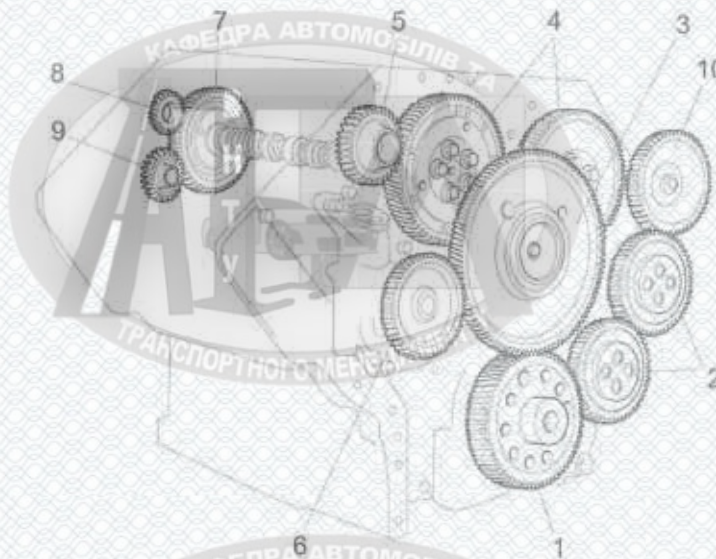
Особливості конструкції газорозподільного механізму, що використовується на V – подібних двигунах SCANIA: 1 - шестерня колінчастого валу; 2 - проміжна шестерня (відбору потужності); 3 - проміжна шестерня; 4 - шестерня приводу розподільчого валу; 5 - шестерня приводу компресора; 6 - шестерня приводу масляного насоса; 7 - передня шестерня розподільчого валу; 8 - шестірня приводу гідравлічного насоса; 9 - шестерня приводу паливопідкачувального насоса; 10 - шестерня приводу механізму відбору потужності.
